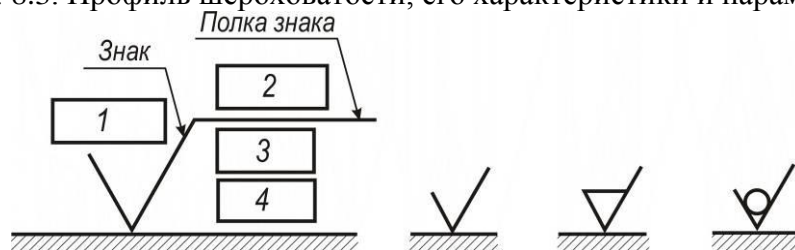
Структура обозначения шероховатости поверхностей на чертежах
